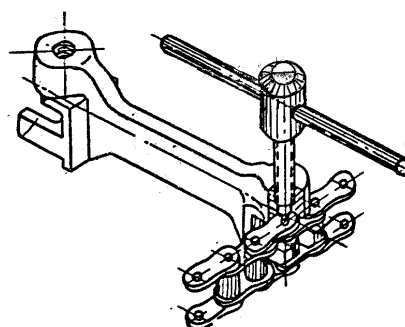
Приспособление для разборки втулочно-роликовых цепей
